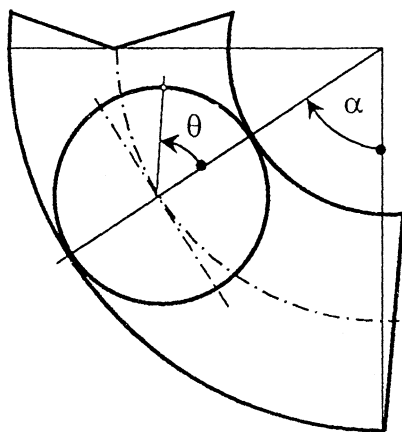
Заготовка коліна та половина її умовної розгортки
